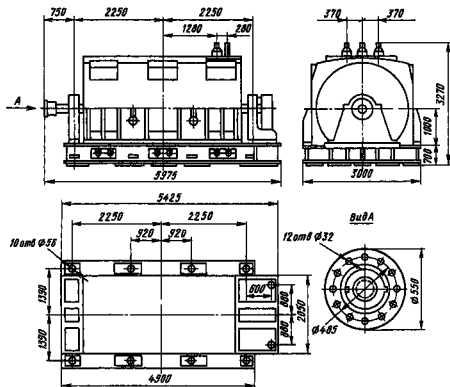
Габаритные и установочно-присоединительные размеры турбогенератора типа Т-20-2
